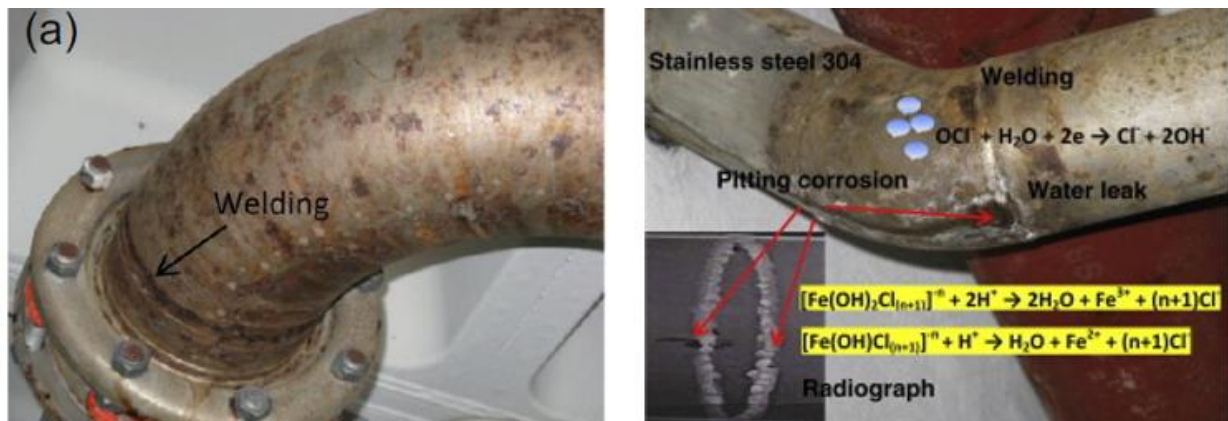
Corrosión por picaduras y en la soldadura transversal en una tubería de acero inoxidable 304 tras 12 años en servicio. [34]
